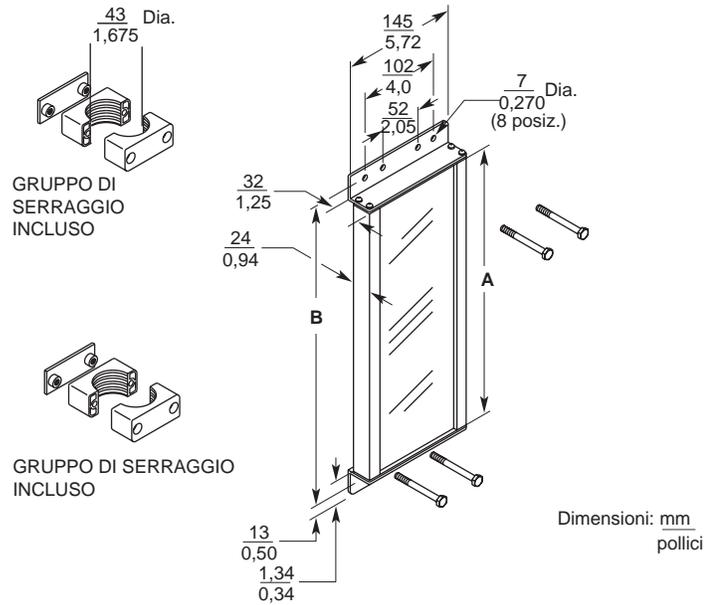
Dimensioni degli specchi (Vedere Tabella 28 per le dimensioni A e B)
